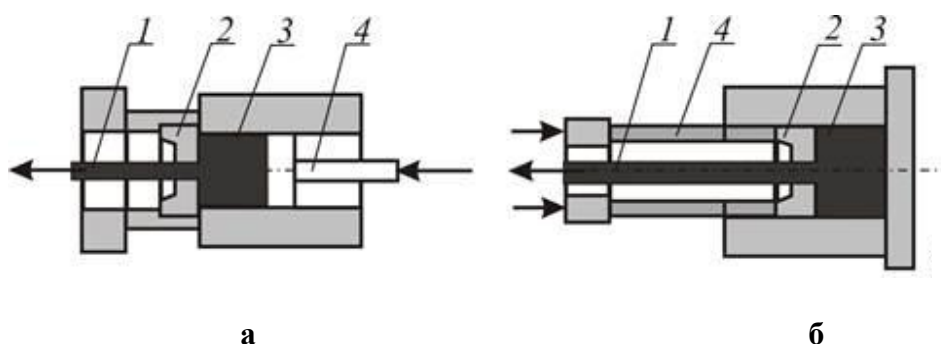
Схема пресування: а – прямим пресуванням б – зворотнім пресуванням: 1 – готовий пруток, 2 – матриця, 3 – заготовка, 4 - пуансон
